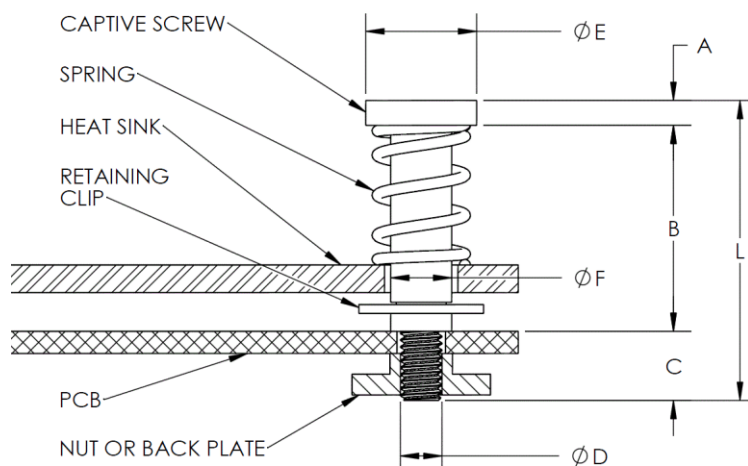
Cargol captador per a subjectar el dissipador a la PCB amb la pressió d'un moll. Font [11].
